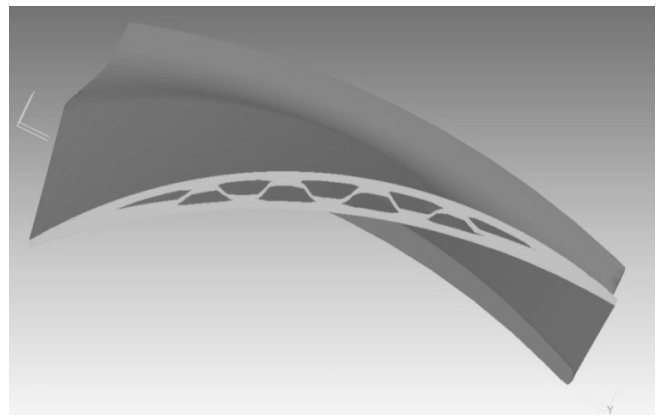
МКЭ - модель трехслойной конструкции в разрезе.
